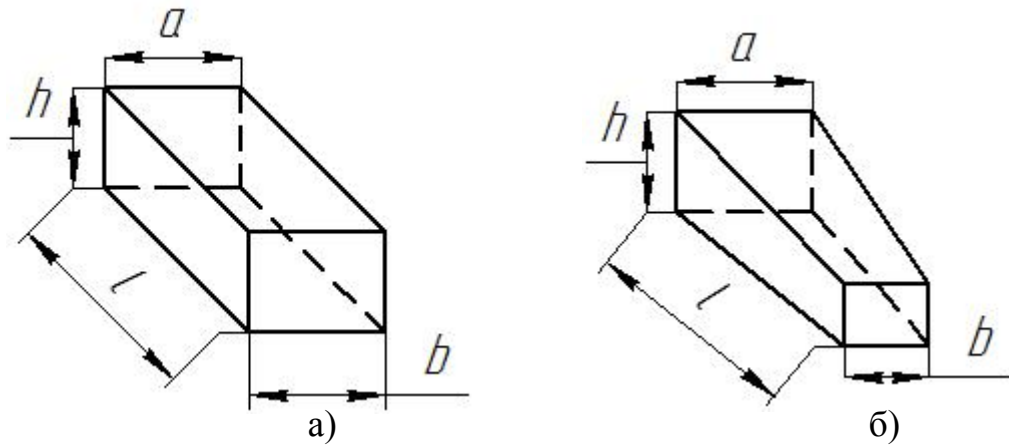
Внешний вид огнеупоров, которые применяются для футеровки цилиндрической части конвертера.
